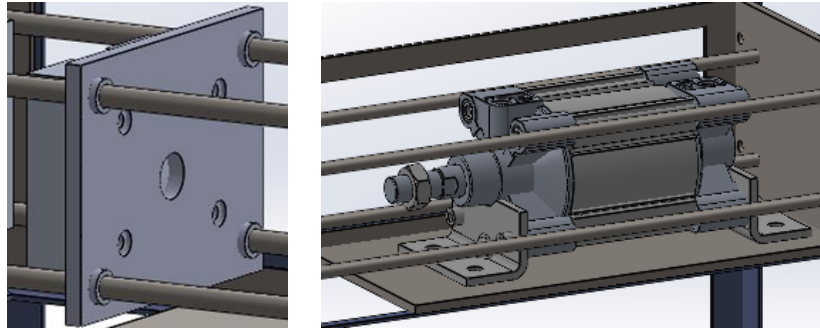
detalle de ensamblaje de molde con cilindro de cierre
